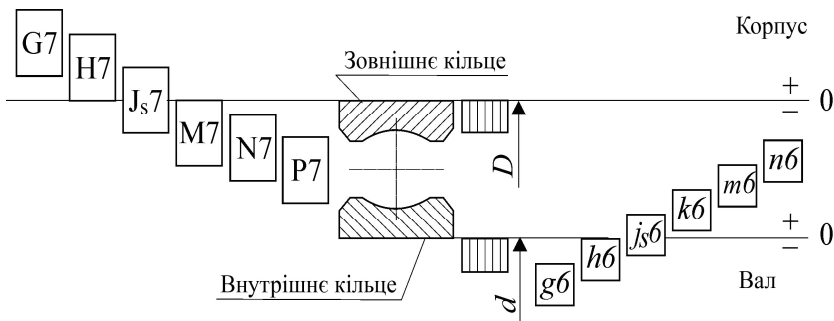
Поле допусків для кілець підшипника кочення
